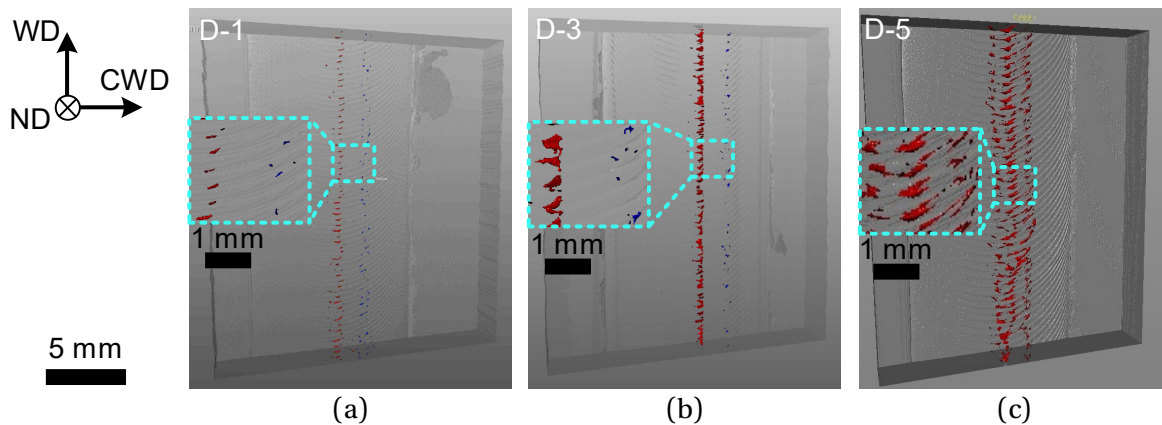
Vue d'ensemble des défauts internes pour une longueur de cordon de 20 mm.
